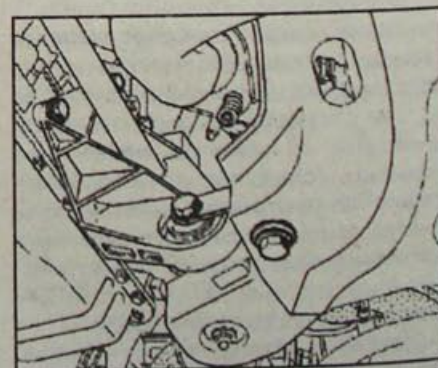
Расположение реактивной тяги крепления двигателя
